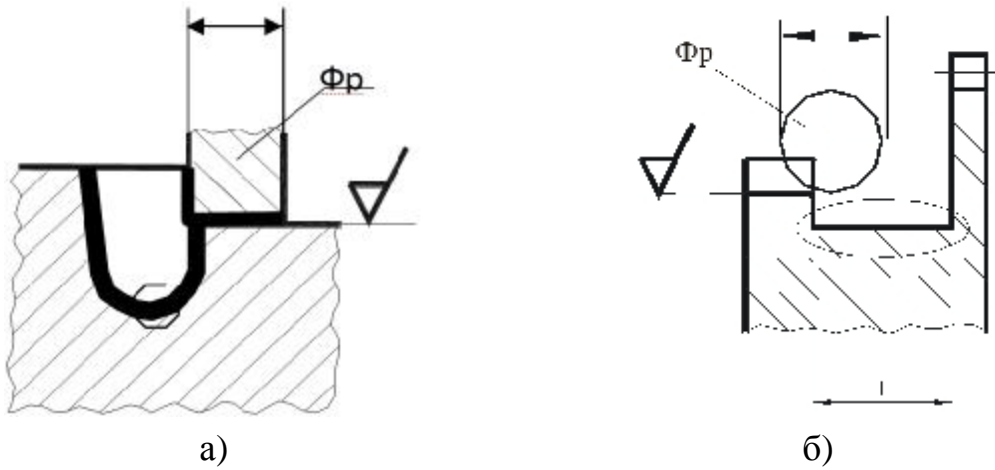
Форма деталі з урахуванням виходу фрези: а – фрезерування виступу в порожнині, виготовлення канавки для виходу фрези; б – Нарізування зубів на колесі фрезою, необхідно передбачити місце для виходу фрези
